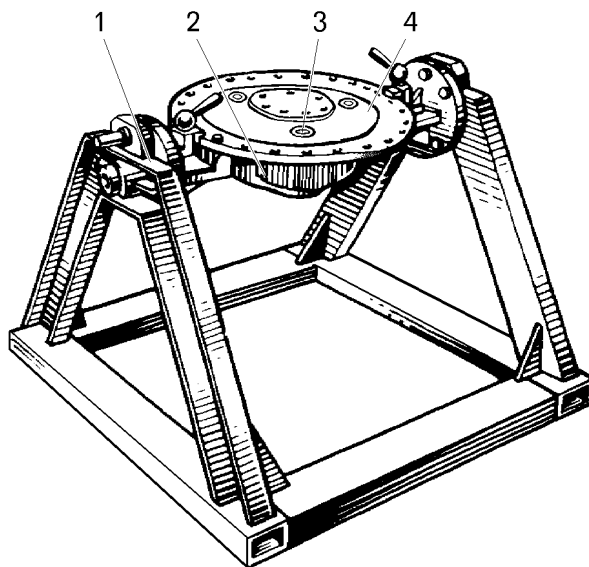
Стенд для разборки и сборки водила колесной передачи:
